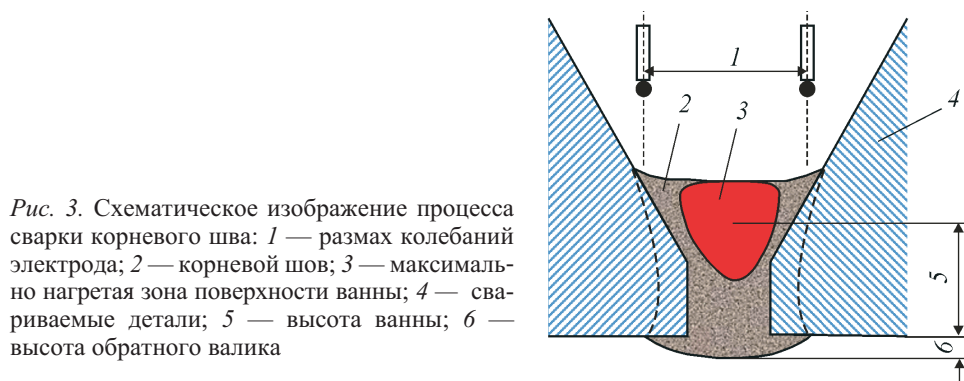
Схематическое изображение процесса сварки корневого шва: 1 — размах колебаний электрода; 2 — корневой шов; 3 — максимально нагретая зона поверхности ванны; 4 — свариваемые детали; 5 — высота ванны; 6 — высота обратного валика
